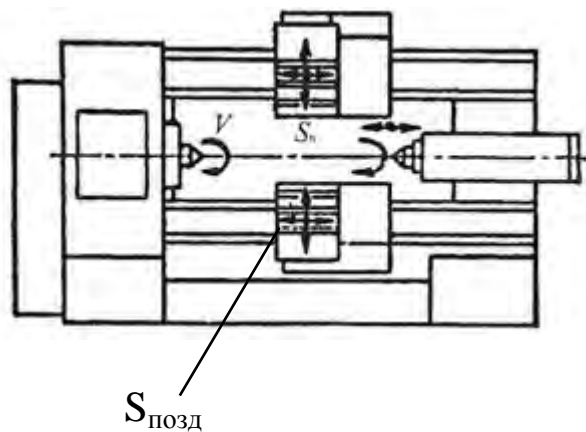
Загальний вид токарного багаторізцевого напівавтомата
